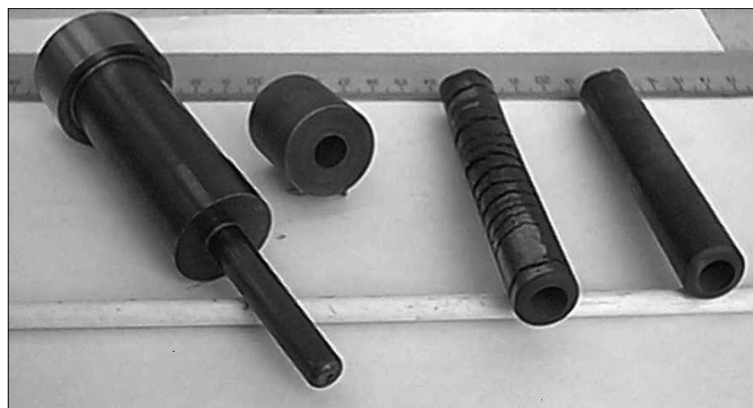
Инструмент и полуфабрикаты детали «направляющая втулка клапана»; слева направо: пуансон с иглой, исходная заготовка, втулка с трещинами, полученная без противодействия, качественная втулка, полученная с использованием противодействия
